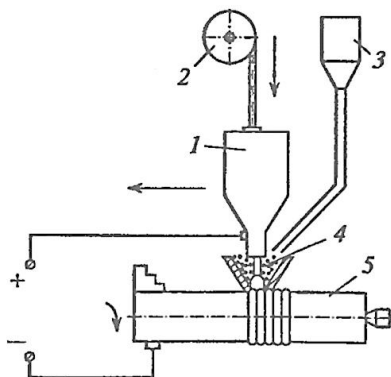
Схема автоматической наплавки цилиндрических деталей под слоем флюса:
